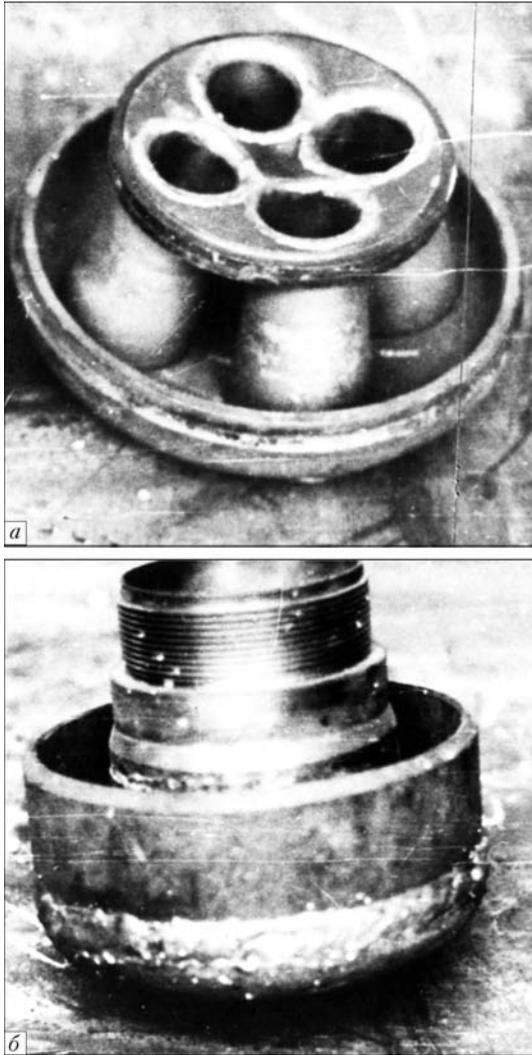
Металлургическая фурма: а – литая заготовка; б – после механической обработки и сварки
